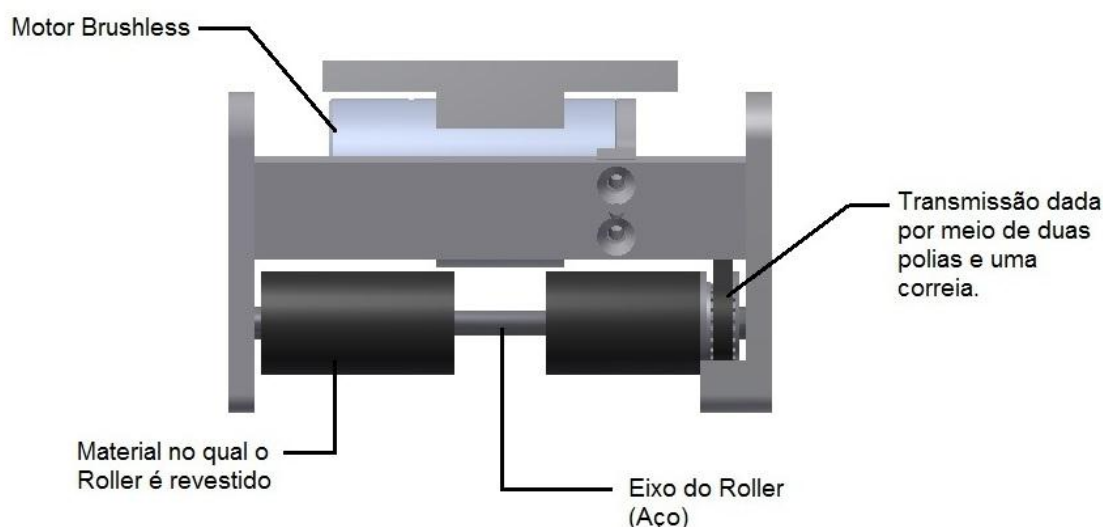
desenho do mecanismo de manipulação da bola utilizado pela equipe
